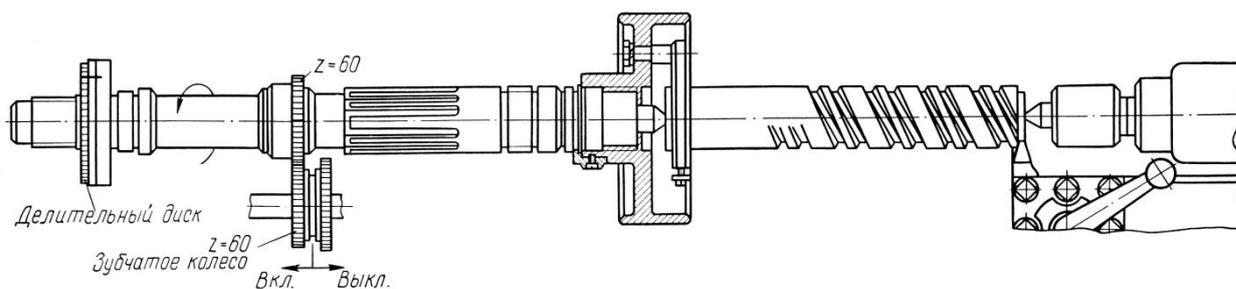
Поворот изделия с помощью делительного устройства шпинделя
